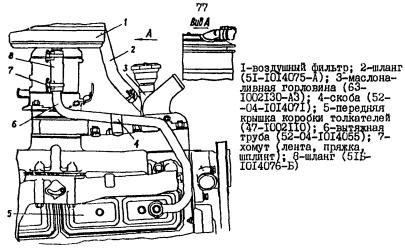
Установка деталей закрытой вентиляции картера двигателя ГАЗ-52-08
